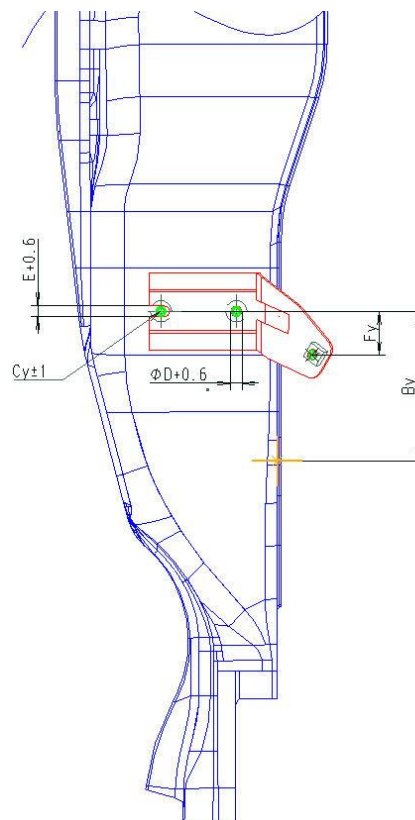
Toleranční řetězec pro bod a, rovina XY
